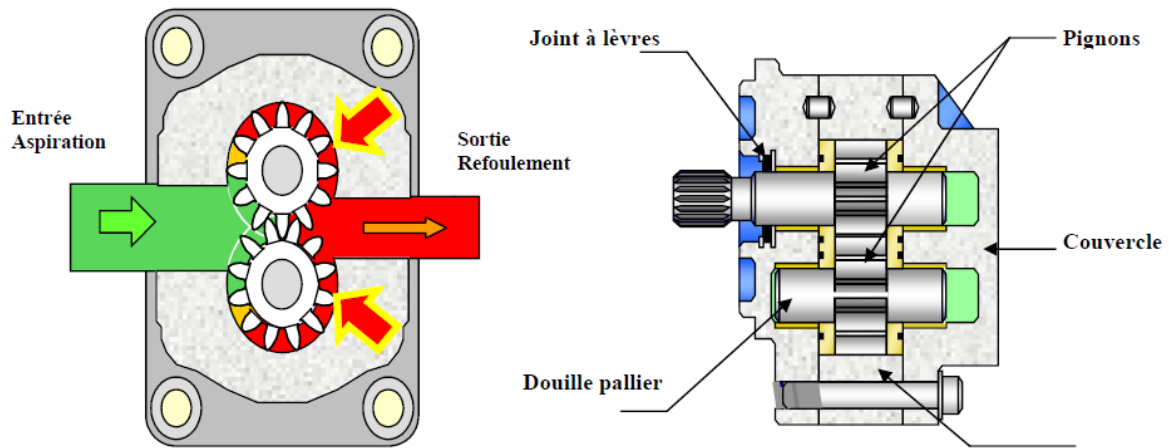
Coupe d'une pompe à engrenages extérieurs
